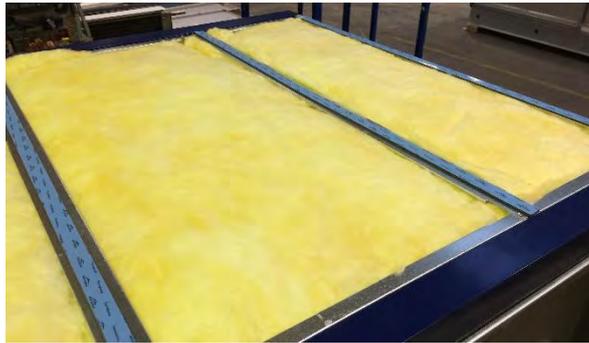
Pièce de la CTA préparée pour l'assemblage de la toiture en tôle
